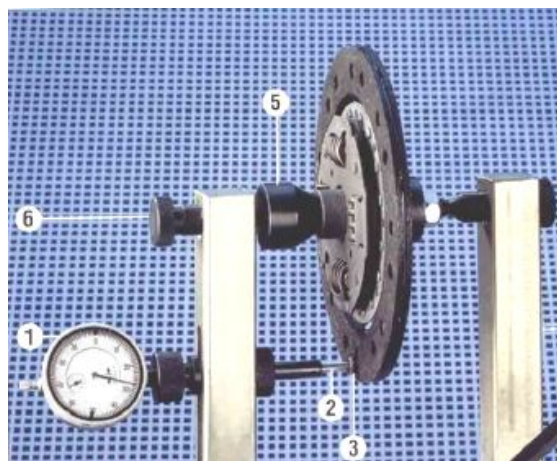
Проверка биения рабочей поверхности ведомого диска.
